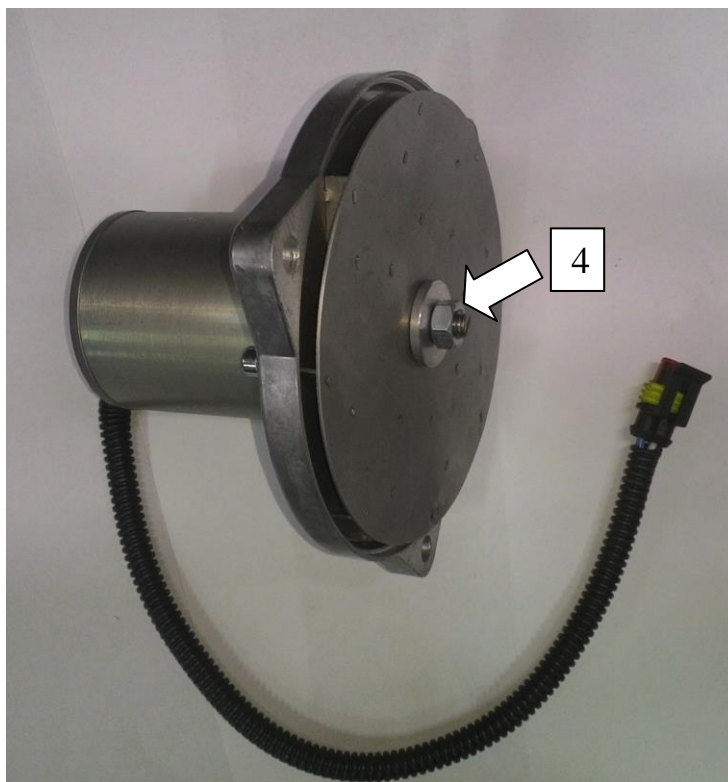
Нагнетатель воздуха подогревателя ПЖД 16-01СТ.
